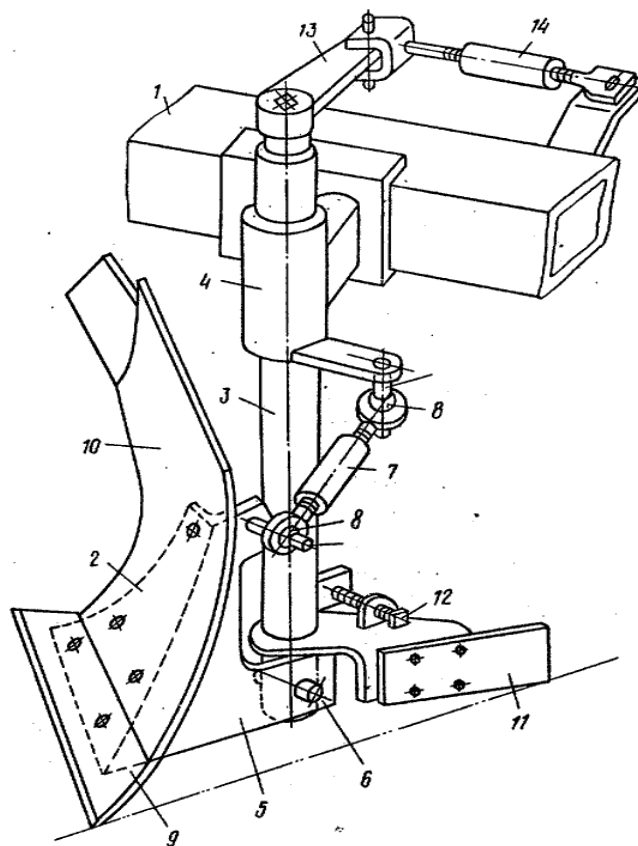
Плуг з регульованою установкою корпусів [52]
